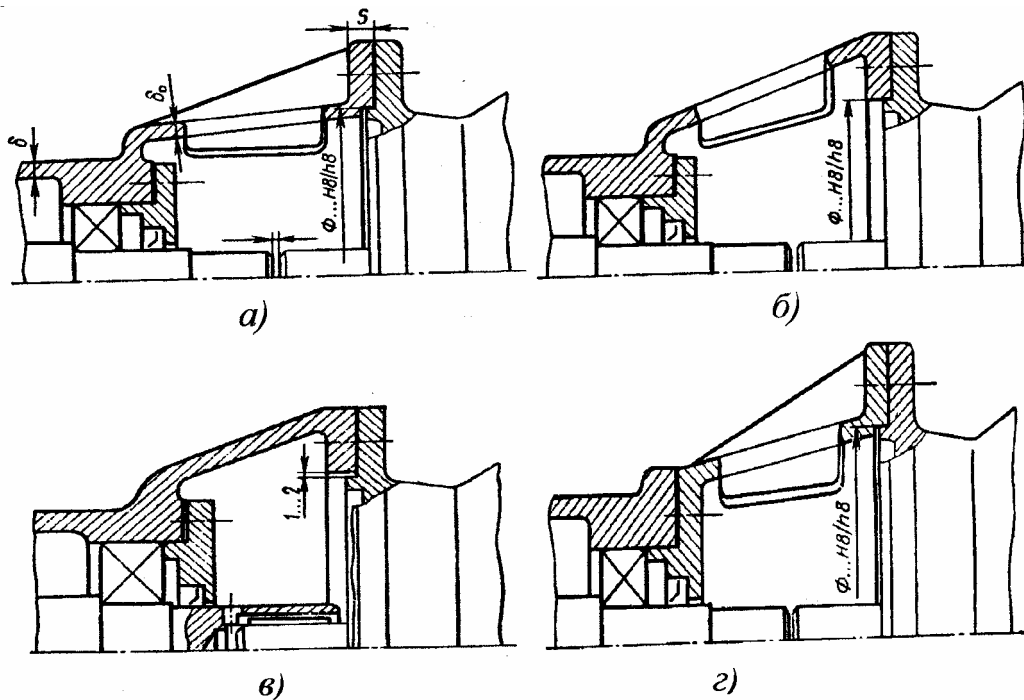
Способы соединения опорного фланца корпуса с фланцем электродвигателя
